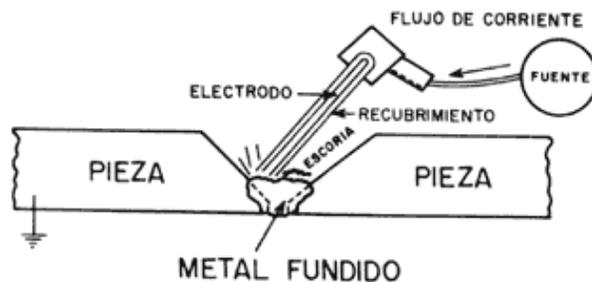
Proceso de soldadura con arco eléctrico. El flujo de una enorme corriente eléctrica produce la fusión de la punta del electrodo y de la superficie de las piezas. El recubrimiento del electrodo ayuda a generar una atmósfera y una escoria que protegen al metal líquido de la oxidación y de otros agentes externos.
